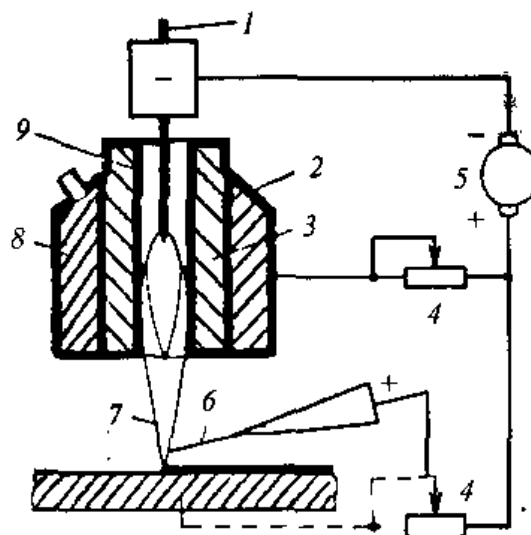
Плазменная наплавка с присадочной проволокой:
